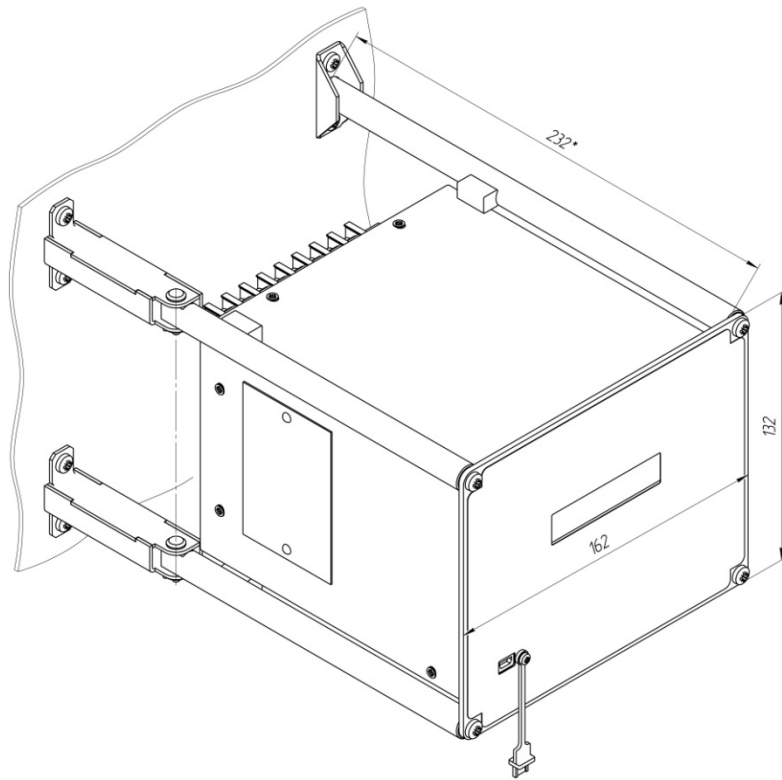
Габаритные и присоединительные размеры устройства РС83-АВ2 (корпус К3, вид монтажа – внутренний)
